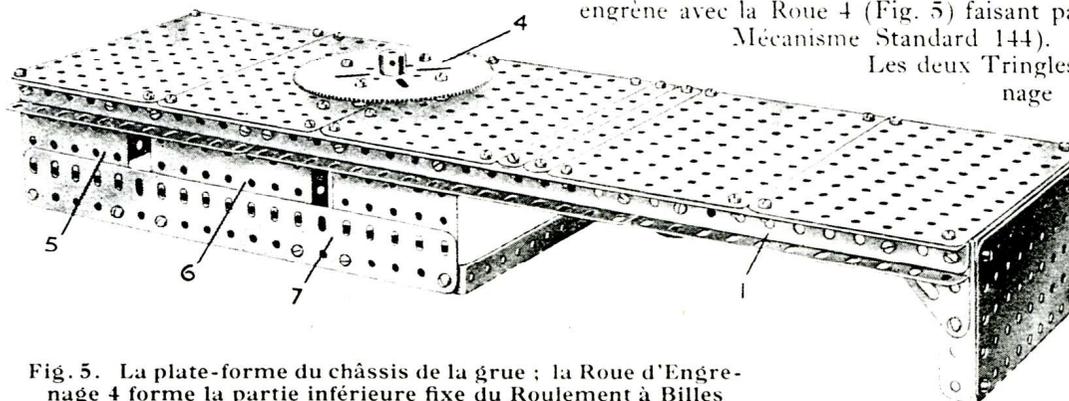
La plate-forme du châssis de la grue ; la Roue d'Engrenage 4 forme la partie inférieure fixe du Roulement à Billes
